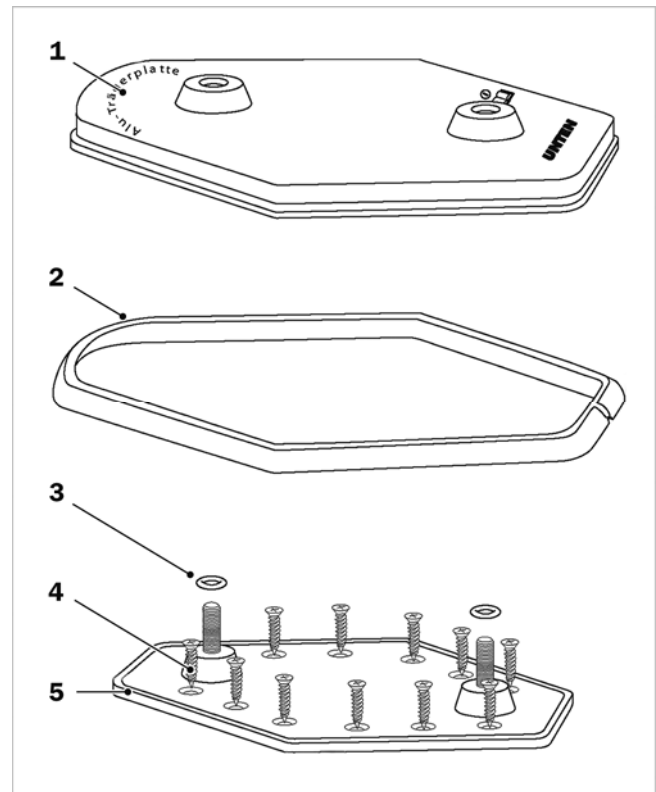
Volumen de suministro del soporte sobre tejado ADH-SF
